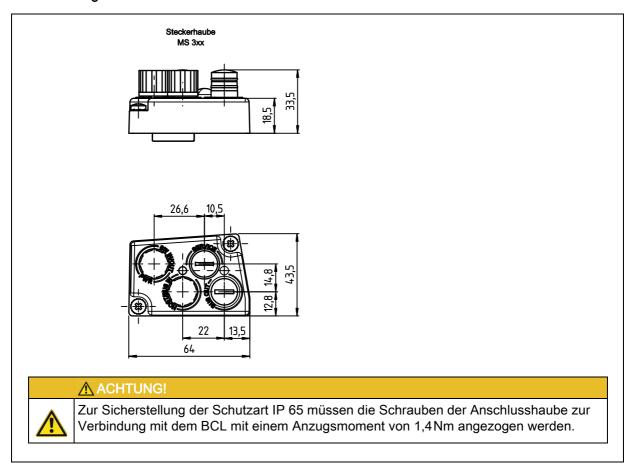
Maßzeichnung Steckerhaube MS 3xx
